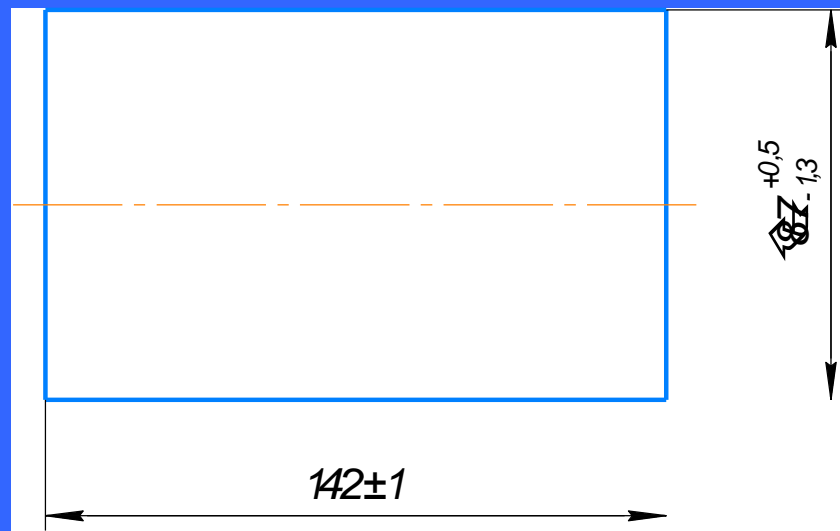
Эскиз заготовки, изготовленной из прутка
